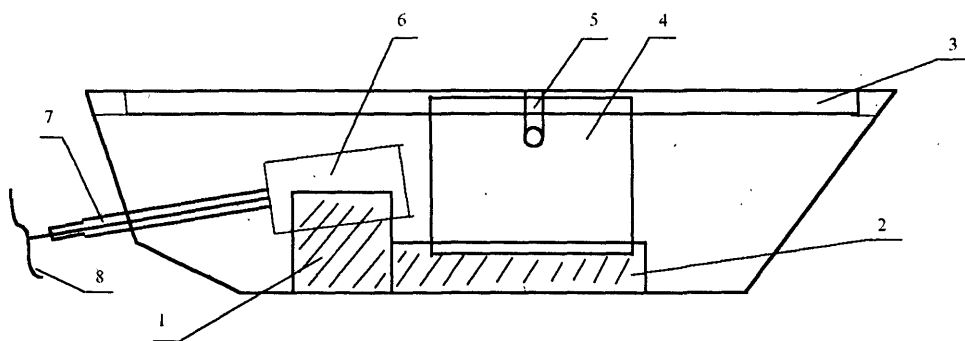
Вид сбоку: 1 — крепежная рейка двигателя; 2 — крепежная рейка редуктора; 3 — палубная крепежная рейка; 4 — редуктор; 5 — отверстие под выходной вал редуктора; 6 — двигатель хода; 7 — кожух вала гребного винта; 8 — гребной винт
